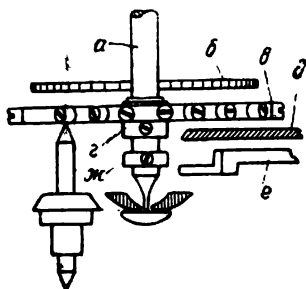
Приспособление для определения размеров оси баланса: *а* — ось баланса; *б* — центральное колесо; *в* — баланс; *г* — муфта с передвигающимся по оси *а* контрольным балансом *д*; *е* — мост анкерной вилки, *ж* — муфта ориентира для установки двойной рольки
